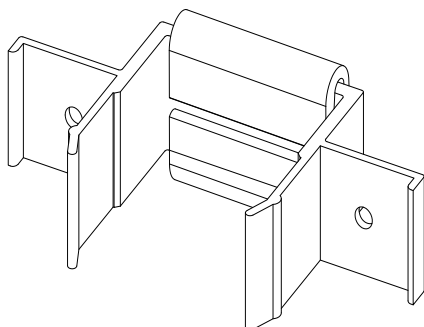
Pieza de cuelgue sistema STB-T-CH (ref. 05.19.062)
